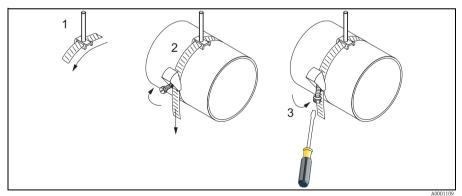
Prémontage des colliers de serrage pour diamètres de conduite DN ≤ 200 (8")
